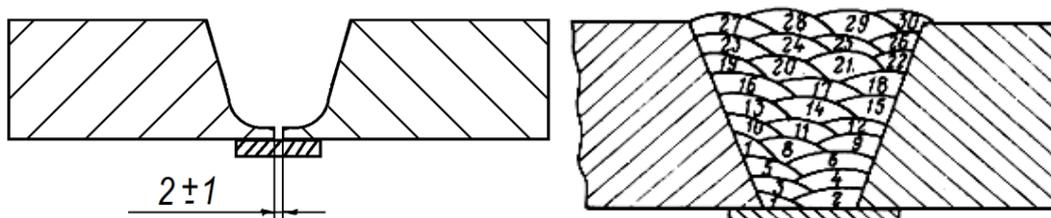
Схемы выполнения валиков в процессе сварки 110 швов, предлагаемая технология: 1 – установка керамической подкладки, 2 – сварка под слоем флюса основного сечения шва, 3 – удаление керамической подкладки
